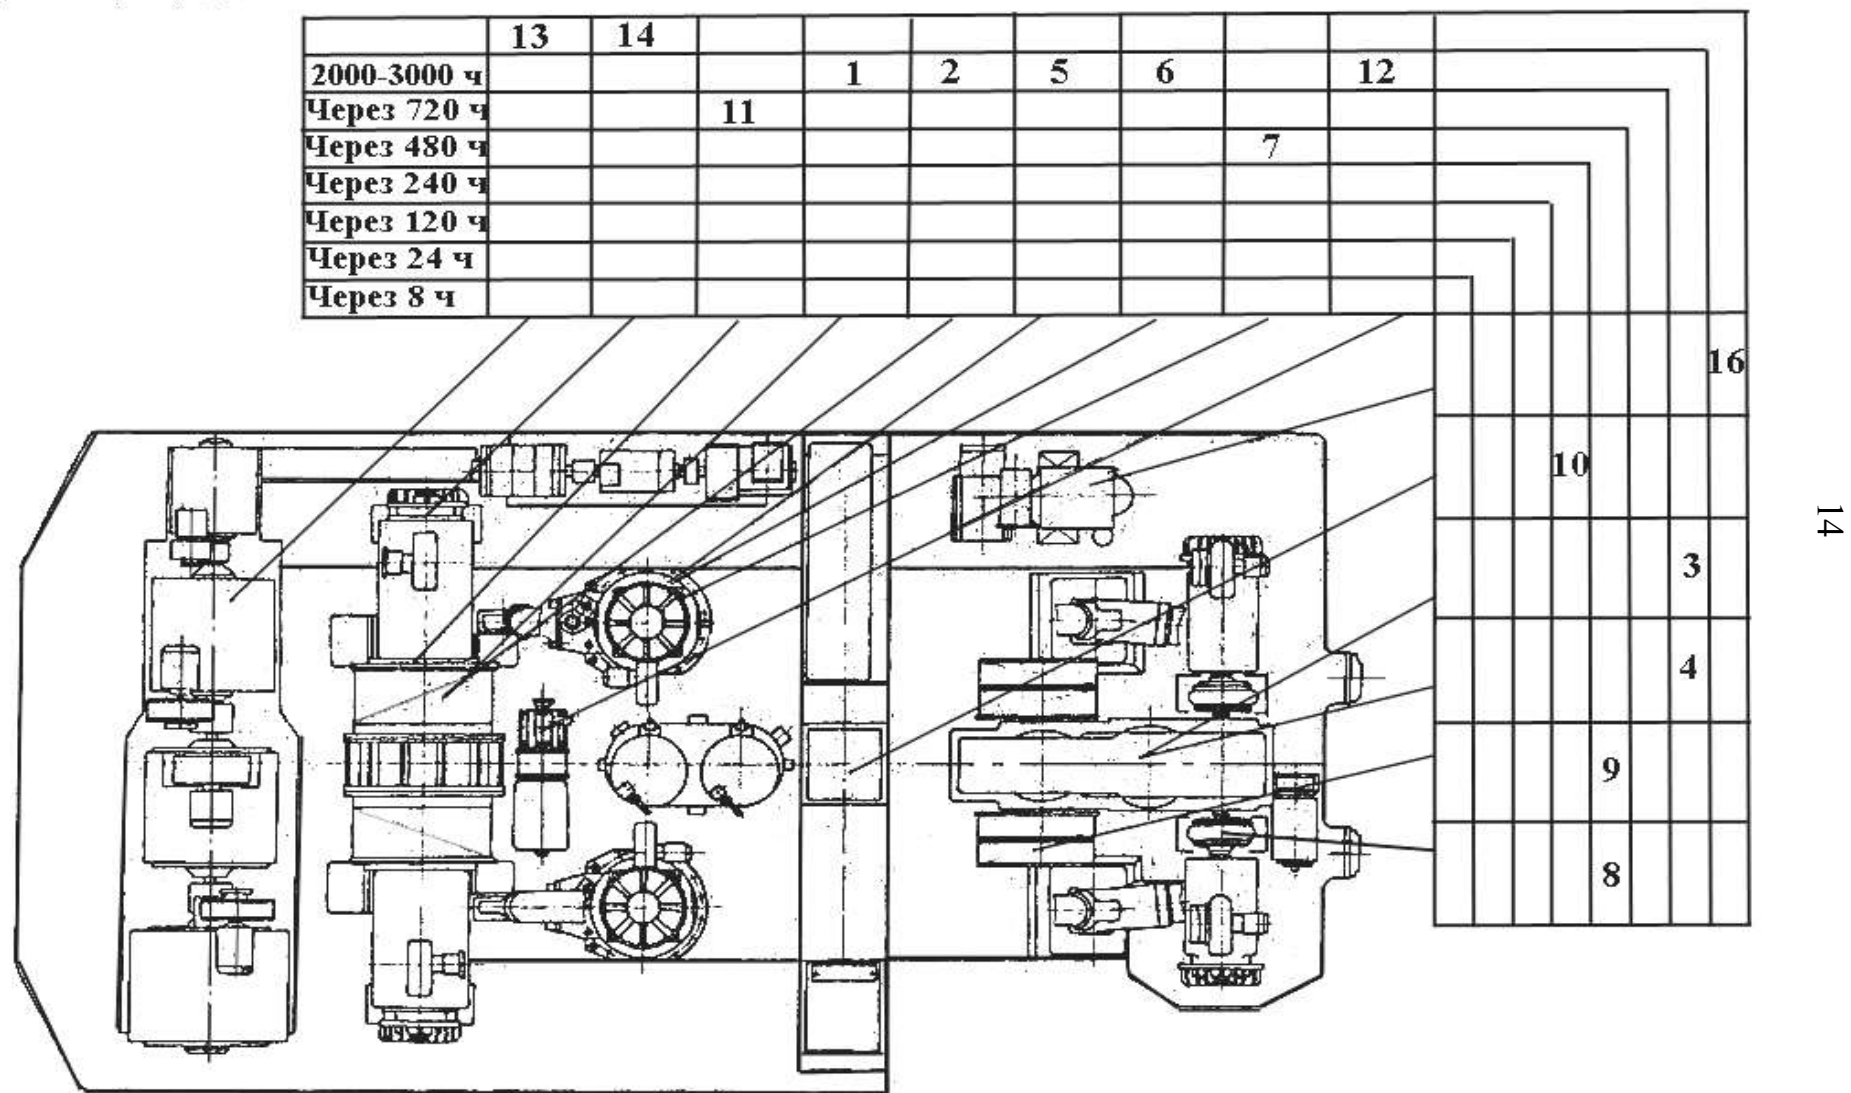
Схема смазки механизмов на поворотной платформе экскаватора ЭКГ-10
